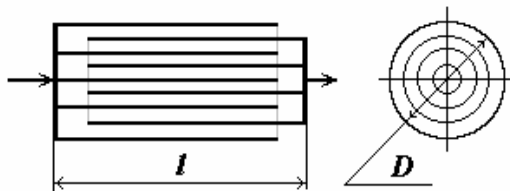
Цилиндрическая намотанная секция с выступающей фольгой
